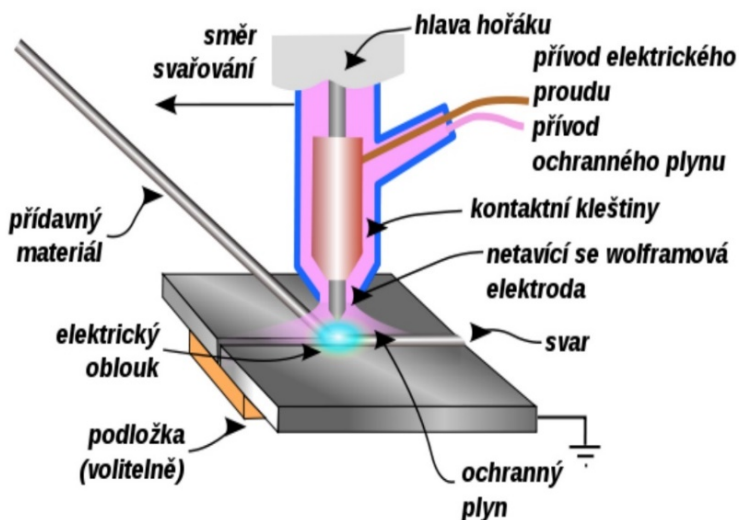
Robotizované svařování, svařování metodou MAG a TIG [3][4]
